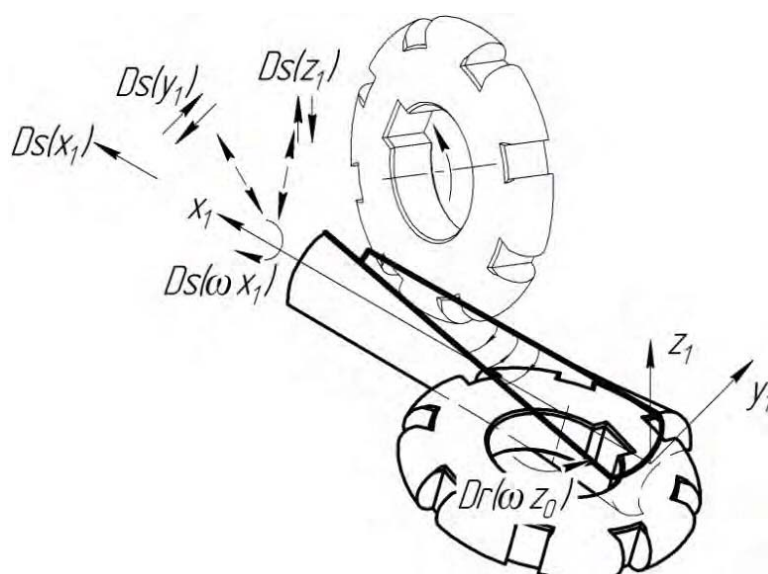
Кинематическая схема обработки винтовой канавки методом нелинейного обката фрезой с тороидальной производящей поверхностью
